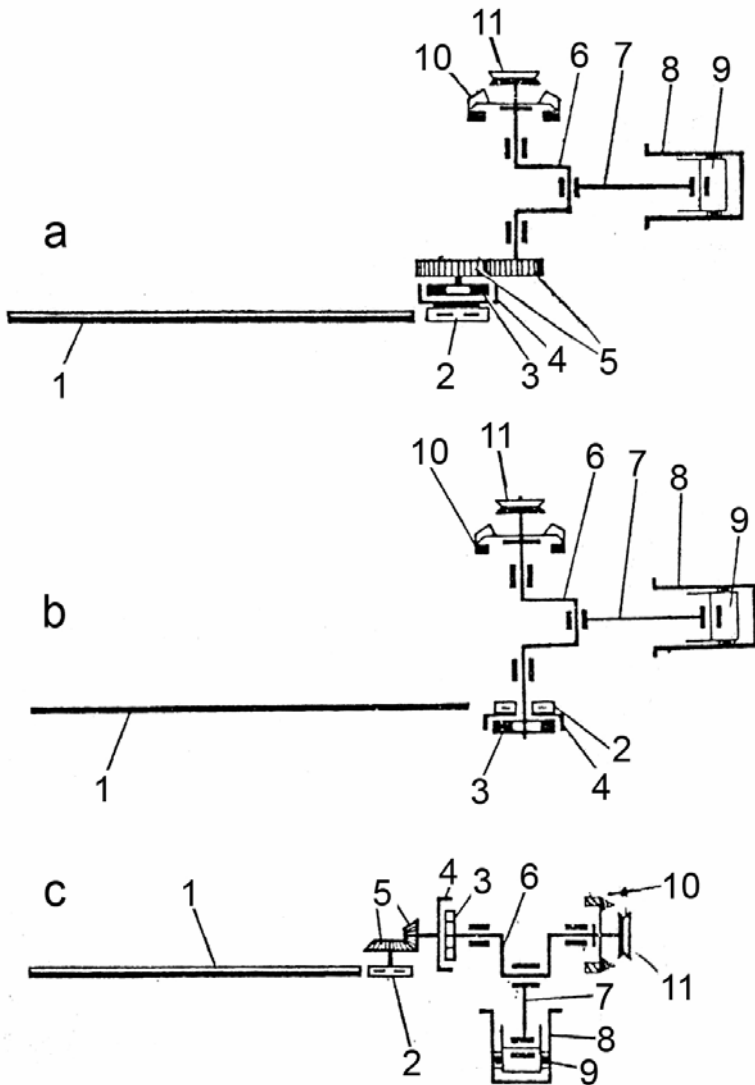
Klasyfikacja pilarek przenośnych [Więsik 2002]
